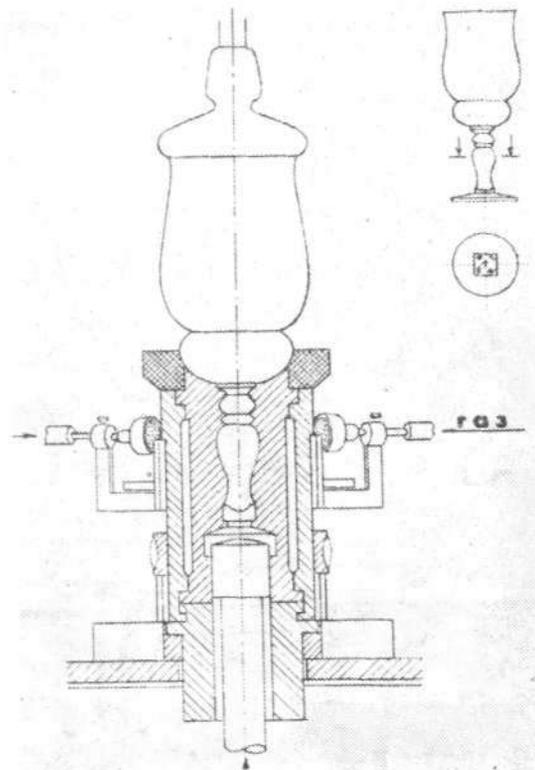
Рабочий узел пневматического пресса для подпрессовки стебля ножки.
